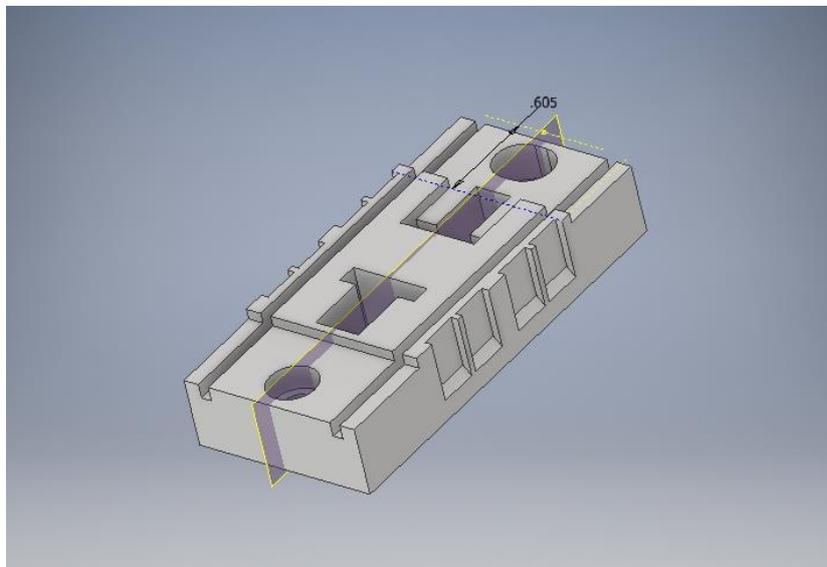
Fixture para ensamble de terminales, modelo de 2 Polos.
